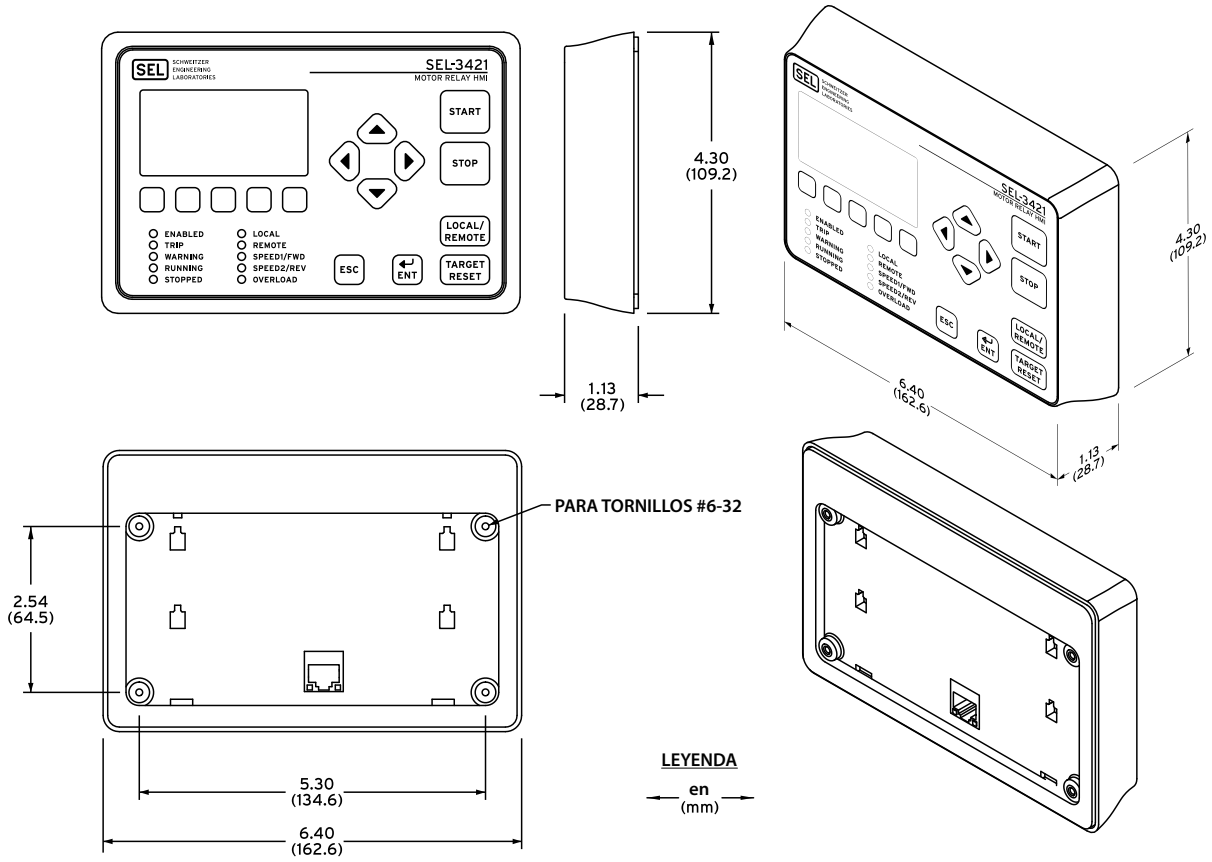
Dibujos de la Instalación de la IHM del Relé de Motor SEL-3421 (Montaje en Panel)
